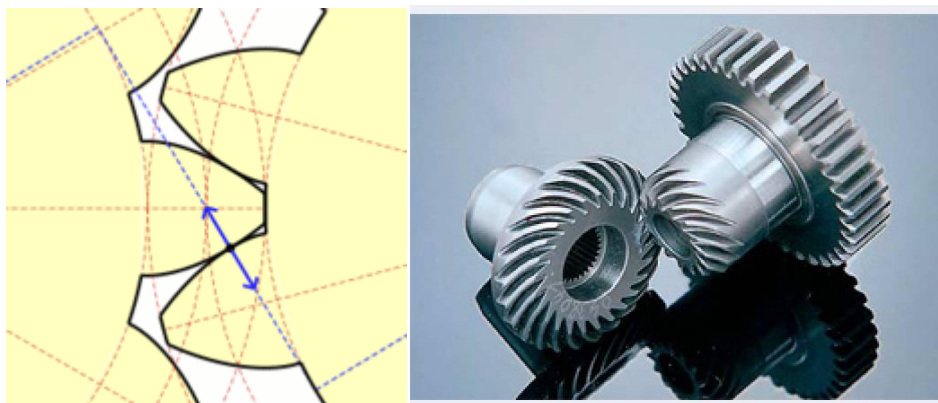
Зубчатые передачи эвольвентного профиля (слева направо)
